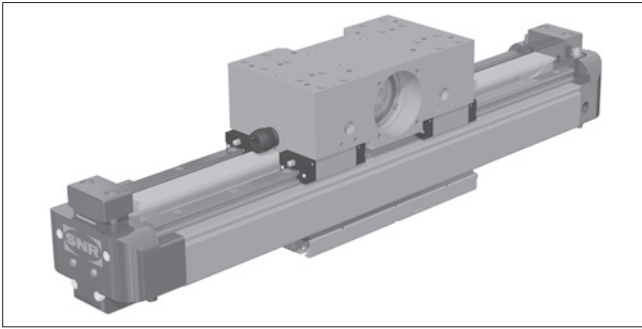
AXS –Teleskopachse, horizontal mit Zahnriemen - Ω - Antrieb
